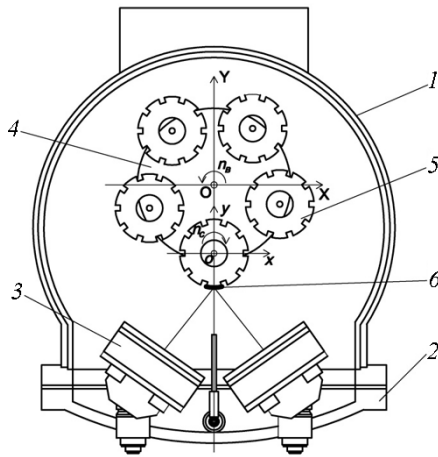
Схема вакуумной установки мод. UniCOAT 600+: 1 — камера; 2 — дверь камеры; 3 — магнетрон; 4 — водило карусели; 5 — спутник планетарного механизма; 6 — напыляемая деталь
